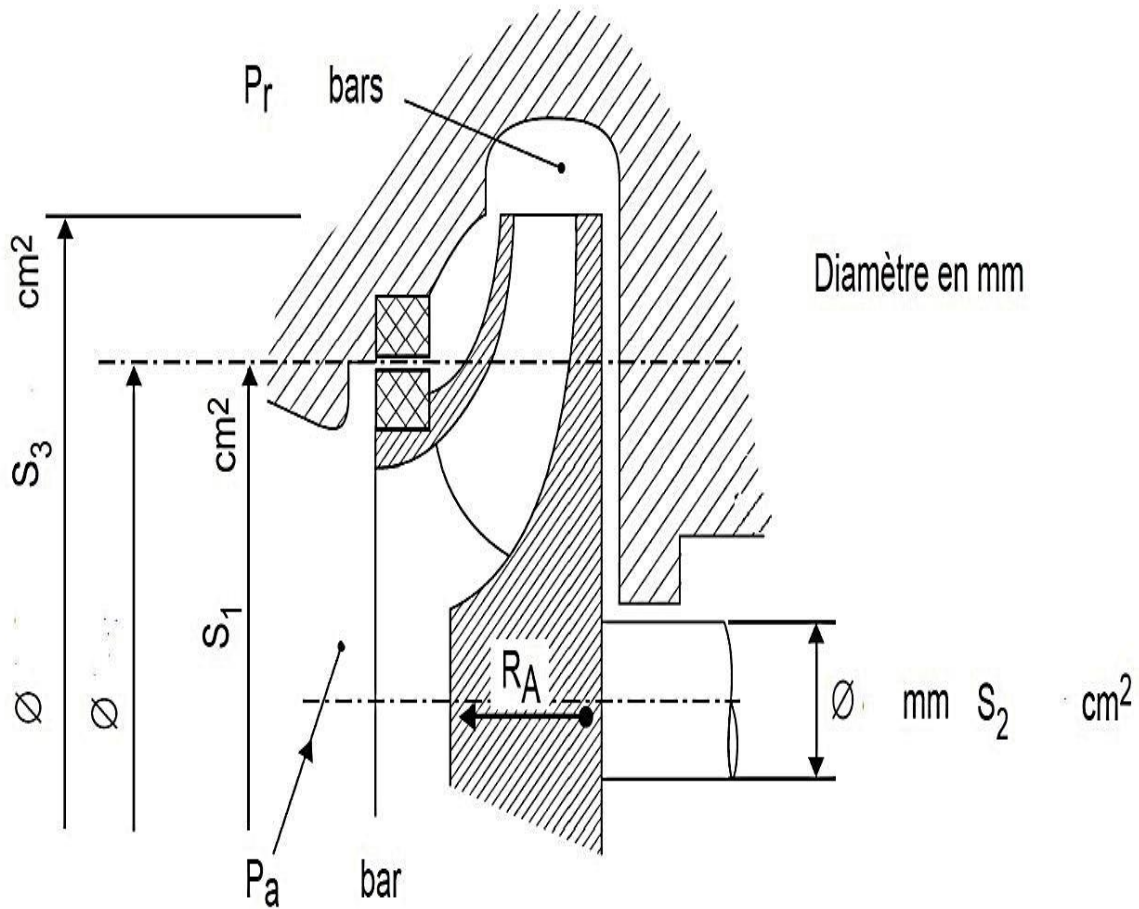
Dimensions principales de la roue pompe centrifuge [8]
